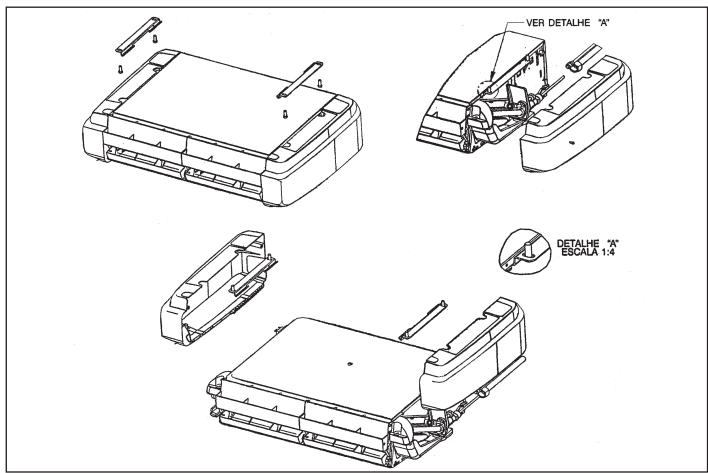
MONTAGEM DO SUPORTE DE FIXAÇÃO
